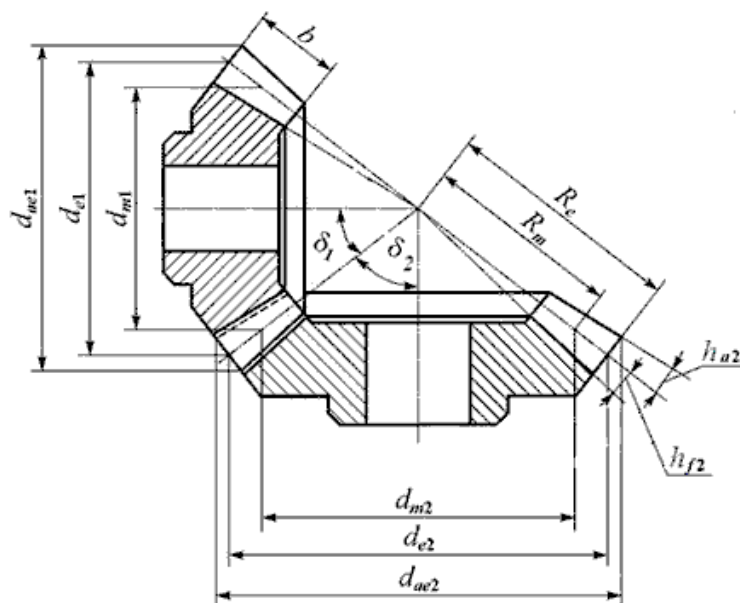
Схема передачи коническими зубчатыми колесами
